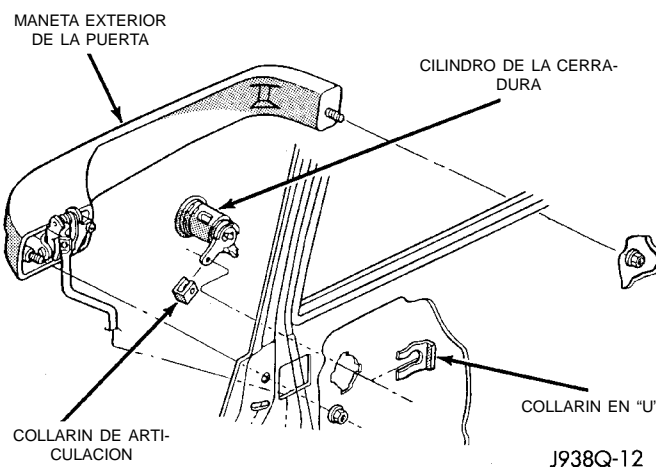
Desmontaje/instalación del cilindro de la cerradura de la puerta
